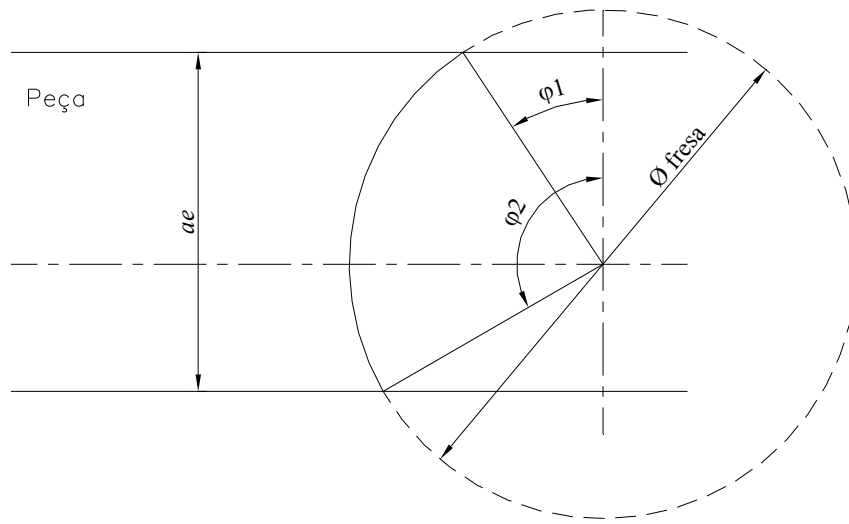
Ângulos de contato no fresamento frontal
